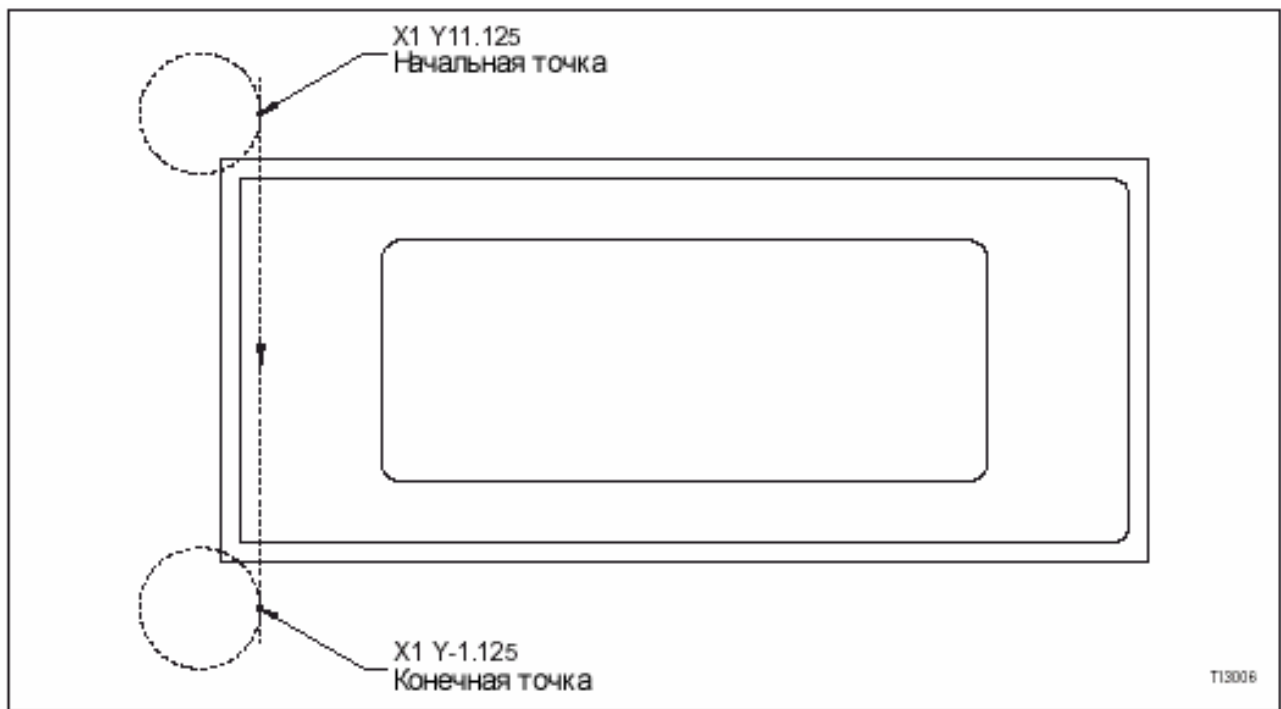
Типовая (стандартная) заготовка: Траектория перемещения инструмента (горизонтальный паз).
